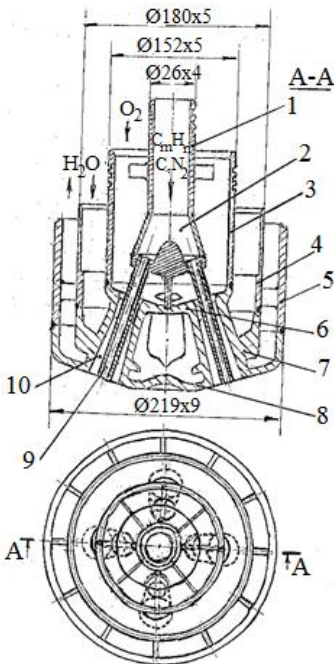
Конструкція 4-х соплової головки обертової паливно-кисневої фурми для нагріву металевго брухту в 160-т конвертері: 1- паливний патрубок; 2- паливний розподільник; 3- кисневий патрубок; 4- проміжний водяний патрубок; 5- зовнішній водяний патрубок; 6- верхня чаша суцільнолитий мідної головки; 7- розподільник води; 8- нижня чаша головки, 9- паливні циліндричні сопла; 10- кисневі сопла Лаваля
